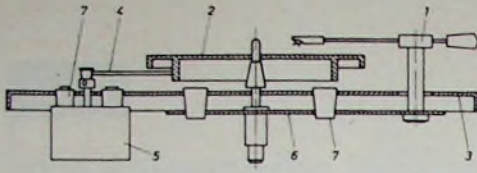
Querschnitt durch das Plattenspielerchassis: 1 Tonarm, 2 Plattenteller, 3 Chassis, 4 Riemen, 5 Motor, 6 Unterchassis, 7 Gummifedern
